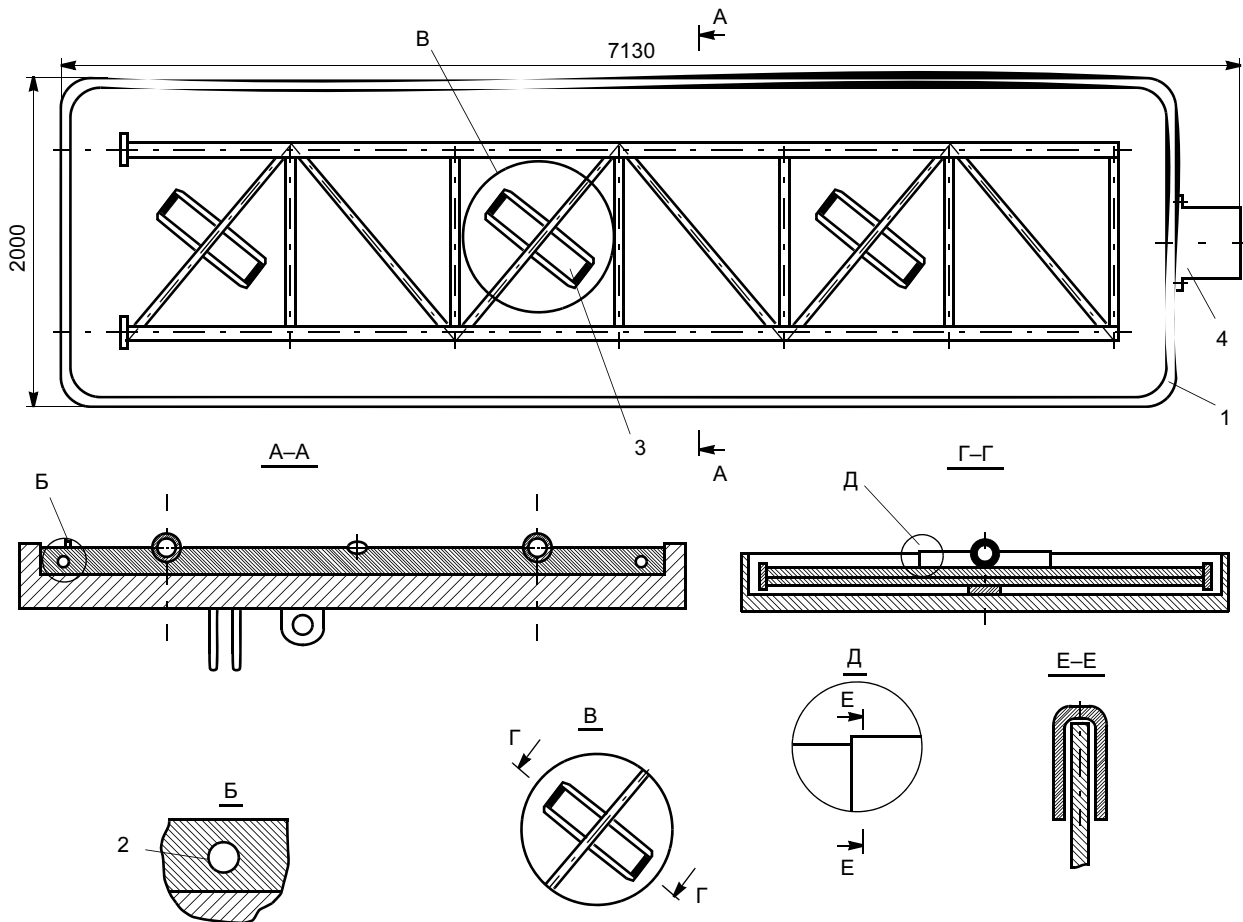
Универсальный стенд для сборки плоских решетчатых металлоконструкций
